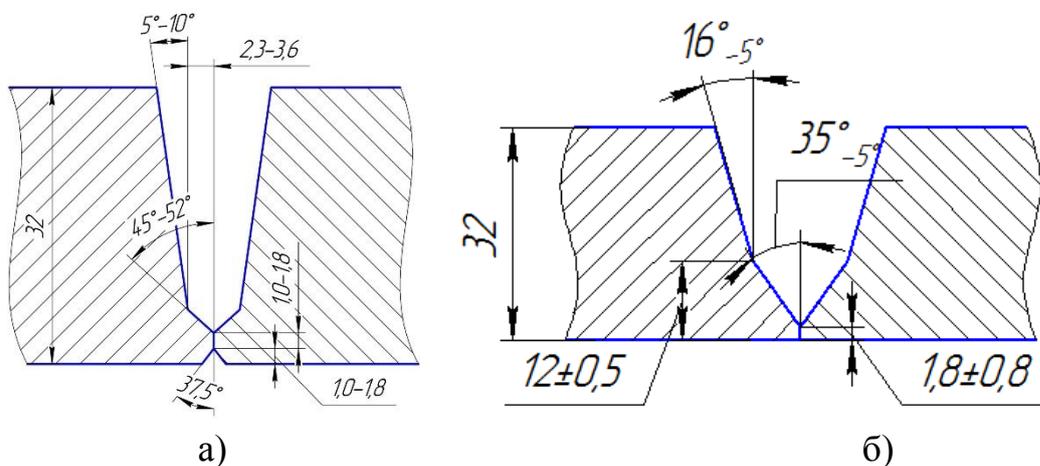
Формы разделок кромок: а) разделка для сварочной головки Р-600; б) разделка для сварочной головки М-300
